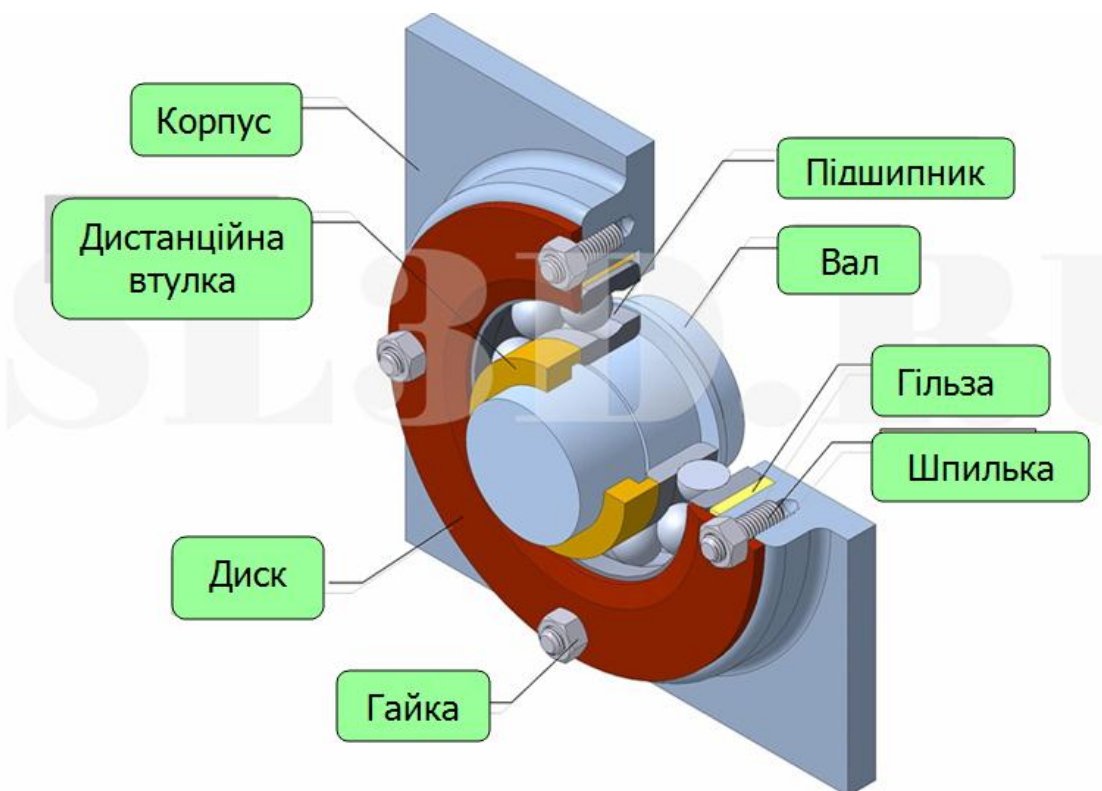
Установка підшипника за допомогою стрічкової гільзи
